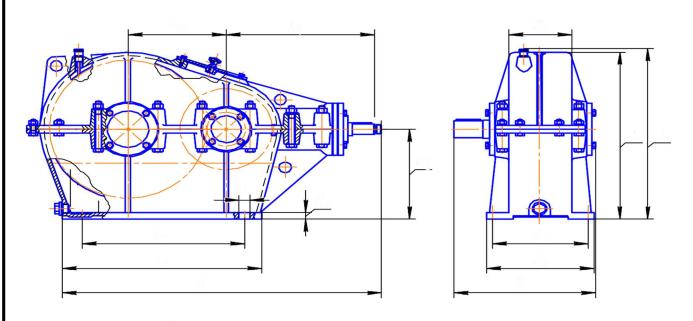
Габаритные и присоединительные размеры коническо-цилиндрического редуктора
